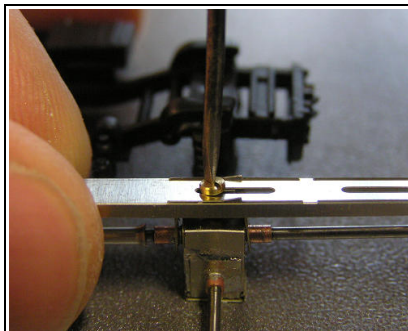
Die Starrachse im Chassisblech mit der Schraube M1x2 befestigen und gewünschten Achsabstand einstellen.
